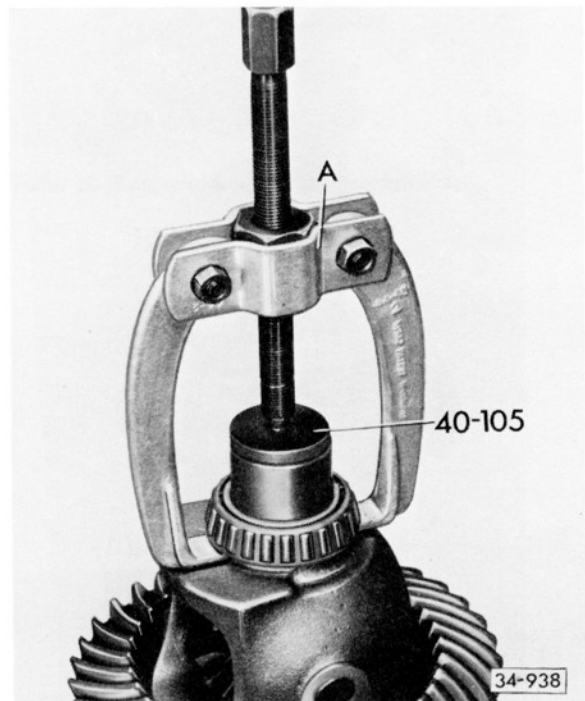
Innenring für kleines Kegelrollenlager vom Gehäuse abziehen
